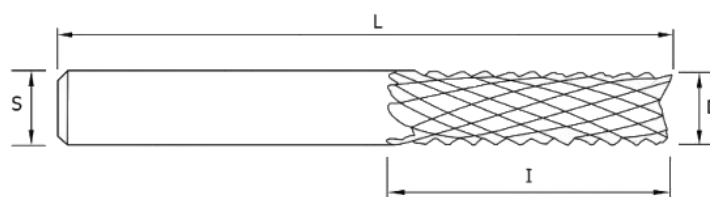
Фреза для обработки композитов типа «кукуруза»
